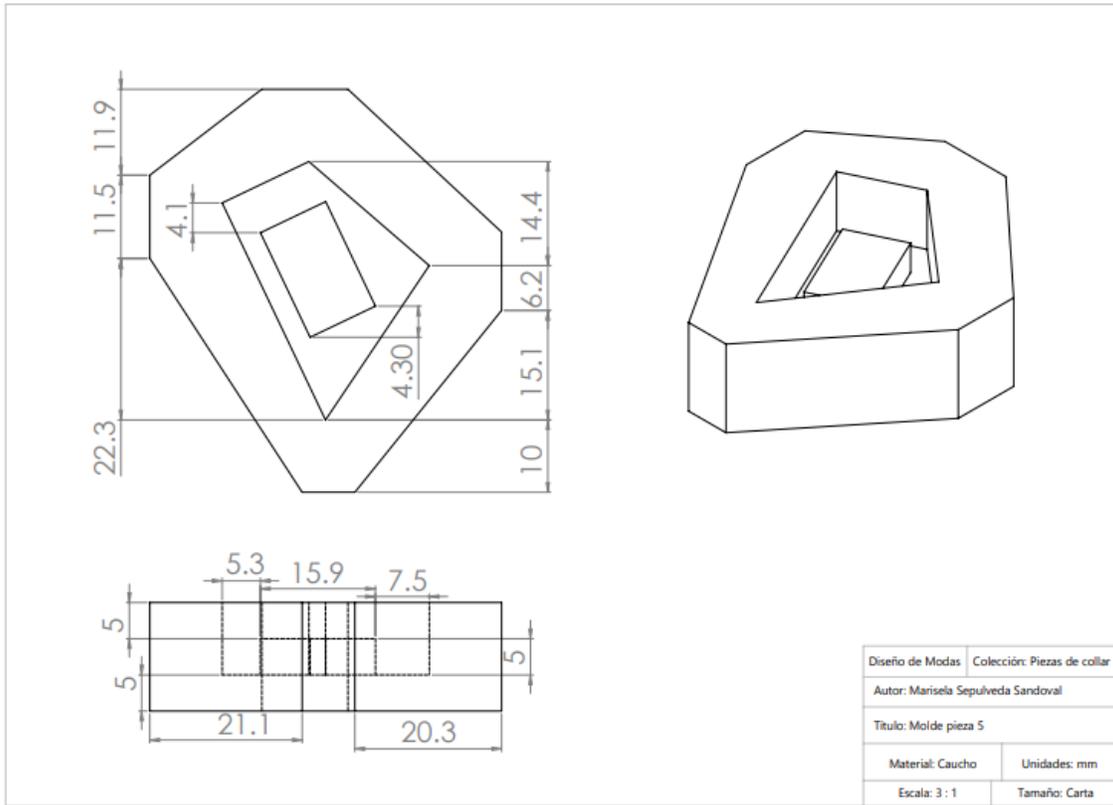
Dimensiones del contra-molde de caucho de la pieza 5.
